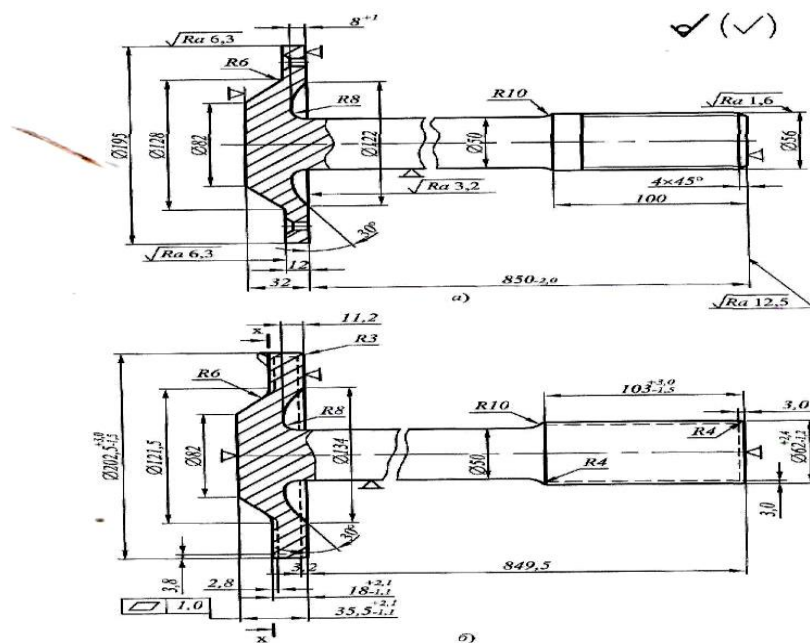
Чертёж детали «полуось» - а и штамповки полуоси – б.
